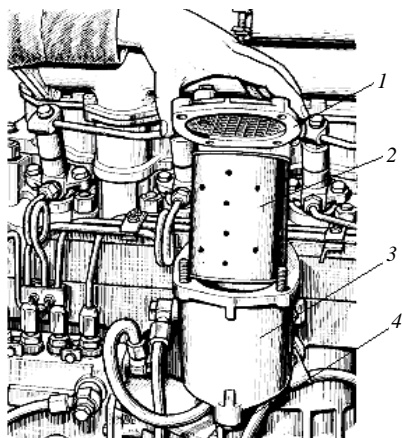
Замена фильтрующего элемента в разборном фильтре тонкой очистки топлива: 1 – крышка фильтра; 2 – фильтрующий элемент; 3 – корпус фильтра; 4 – пробка
